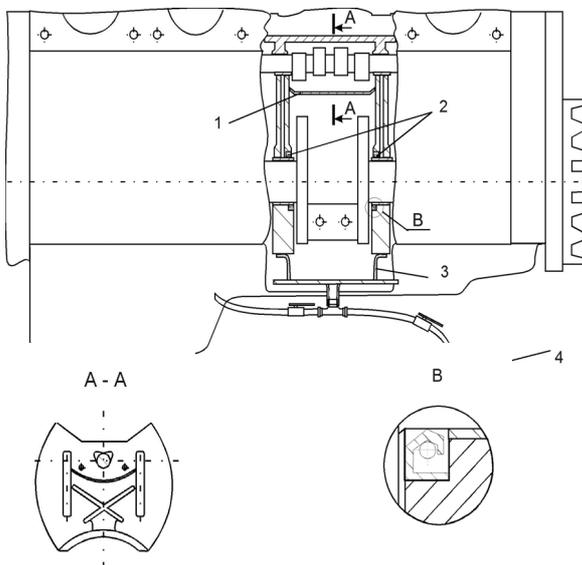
Подвод масла к 1-й шатунной шейке по оси коленчатого вала из системы смазки двигателя через внешний масляный канал
